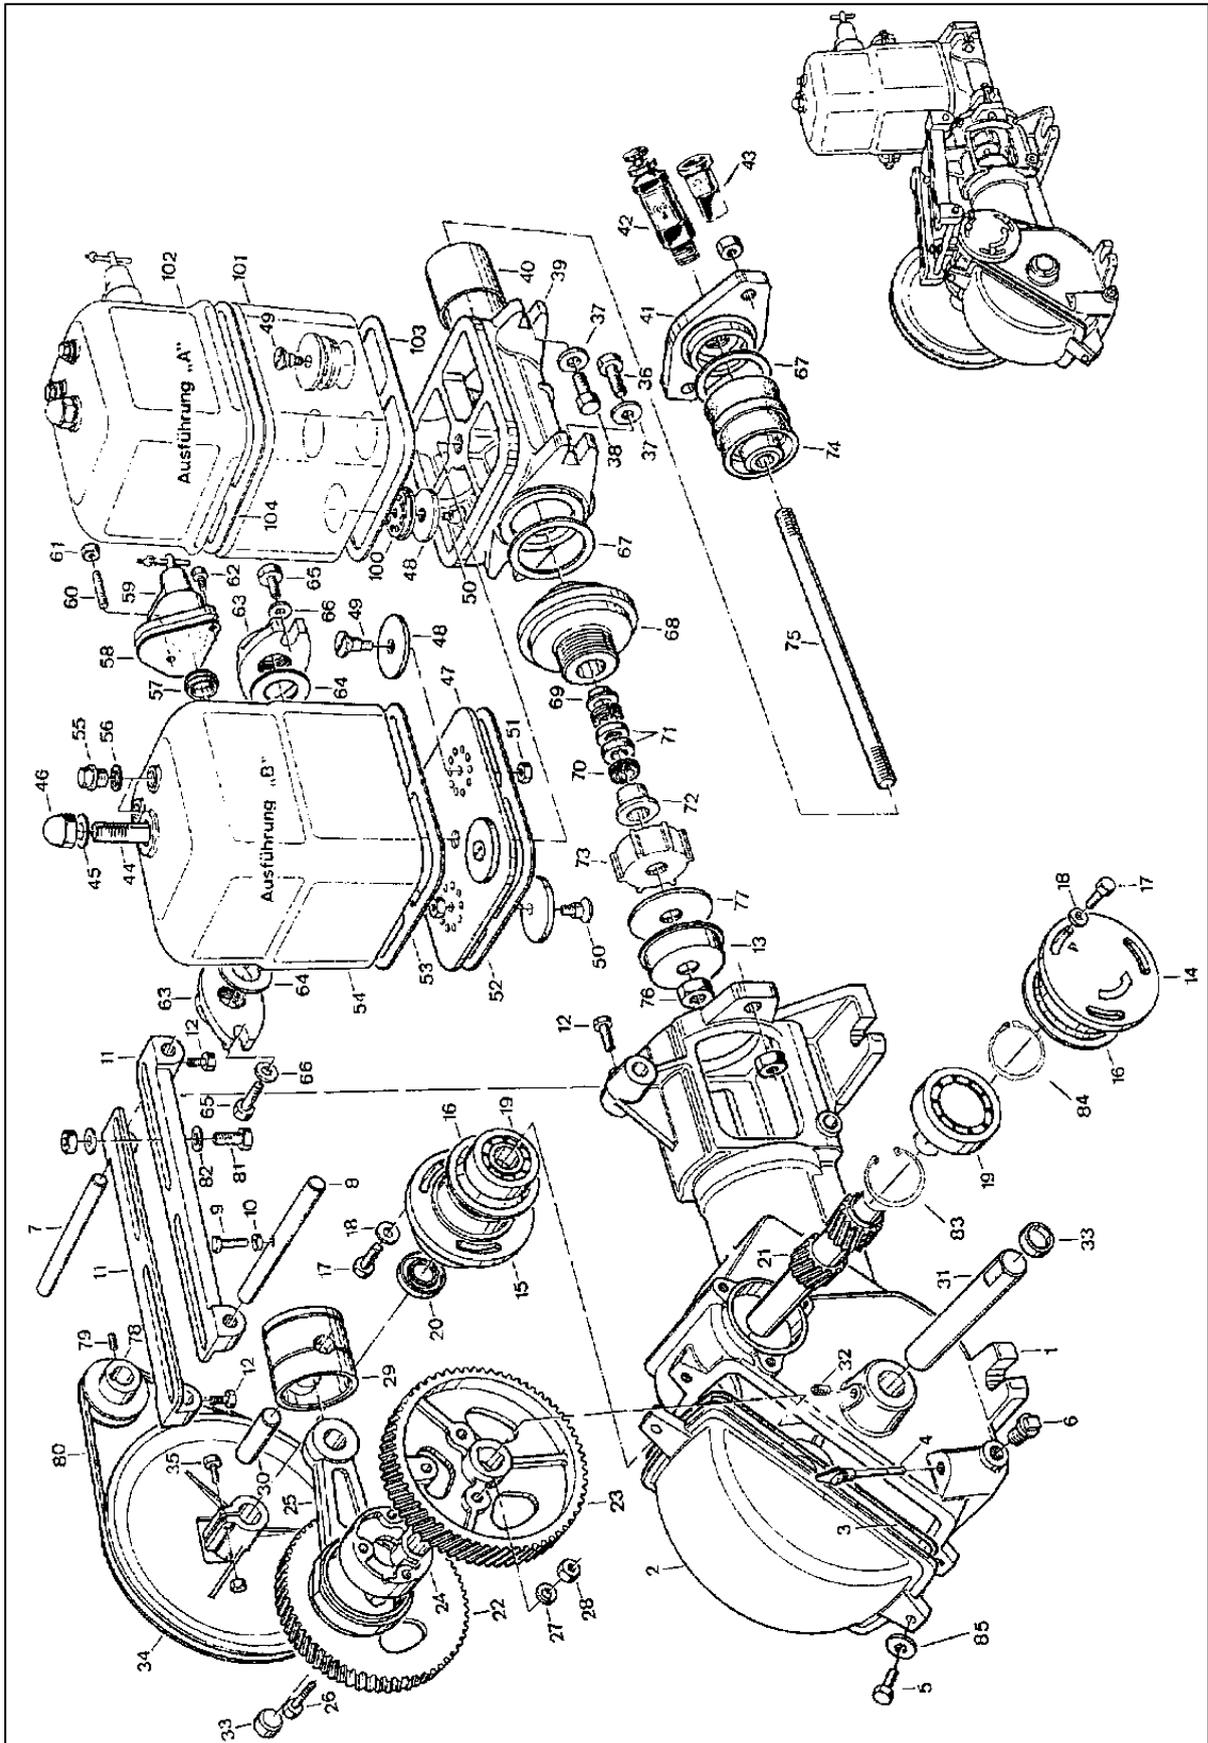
Explosionszeichnung der Kolbenpumpe LG 100-400
